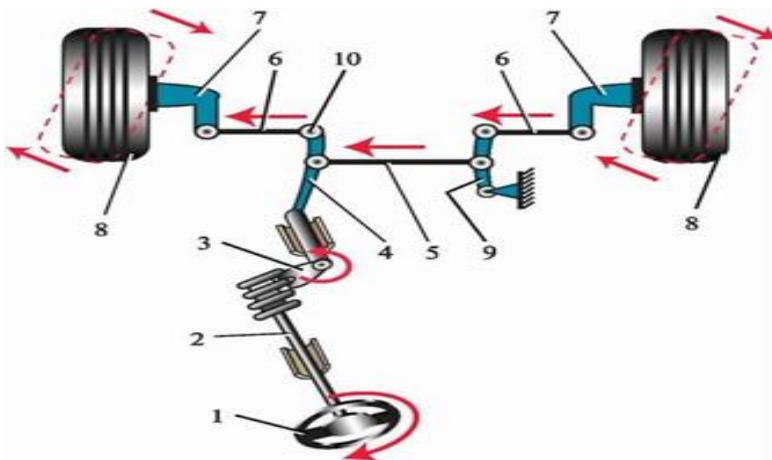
Схема рулевого управления с механизмом типа "червяк-ролик": 1 – рулевое колесо; 2 – рулевой вал с червяком; 3 – ролик с валом сошки; 4 – рулевая сошка; 5 – средняя тяга; 6 – боковые тяги; 7 – поворотные рычаги; 8 – передние колеса автомобиля; 9 – маятниковый рычаг; 10 – шарниры рулевых тяг
